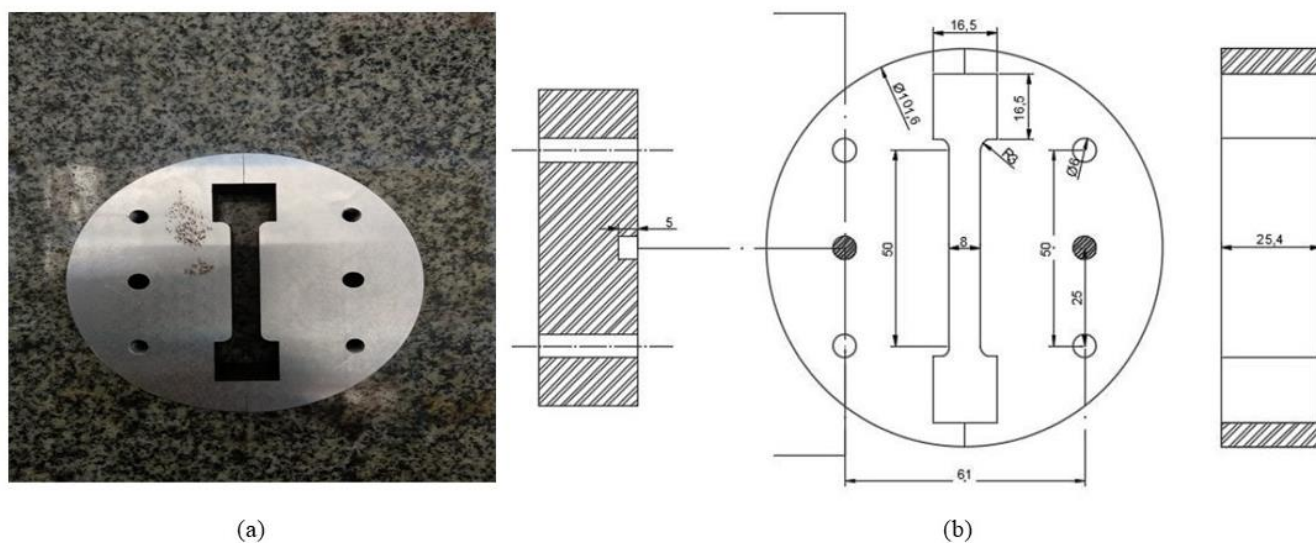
(a) Molde de vazamento, (b) dimensões do molde.
